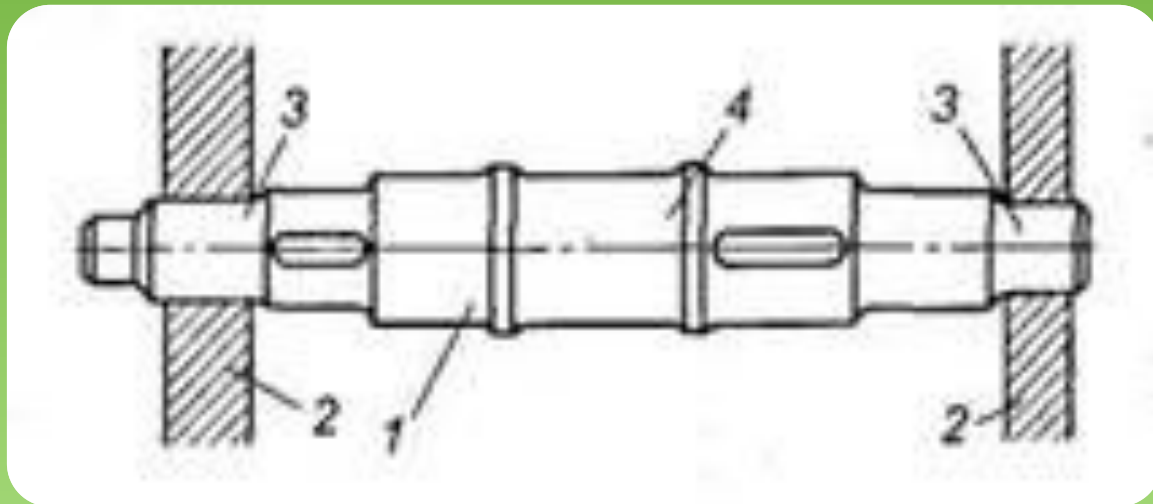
Прямой вал: 1 — вал; 2 — опоры вала; 3 — цапфы; 4 — шейка
